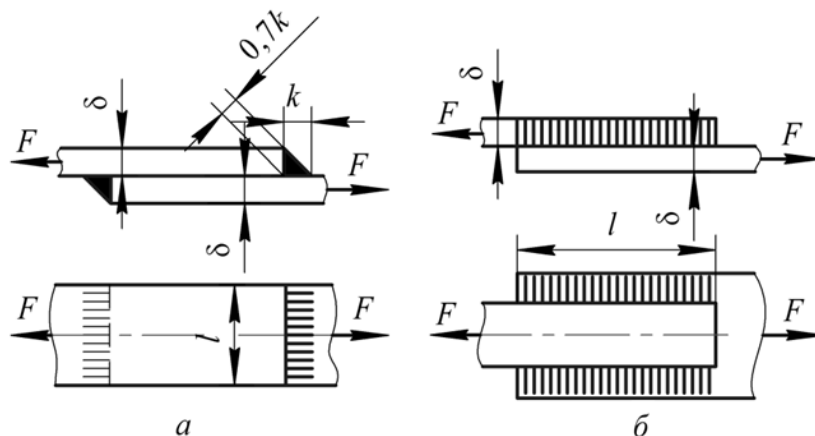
Сварное соединение угловым лобовым швом, нагруженное перпендикулярной растягивающей (сжимающей) силой
